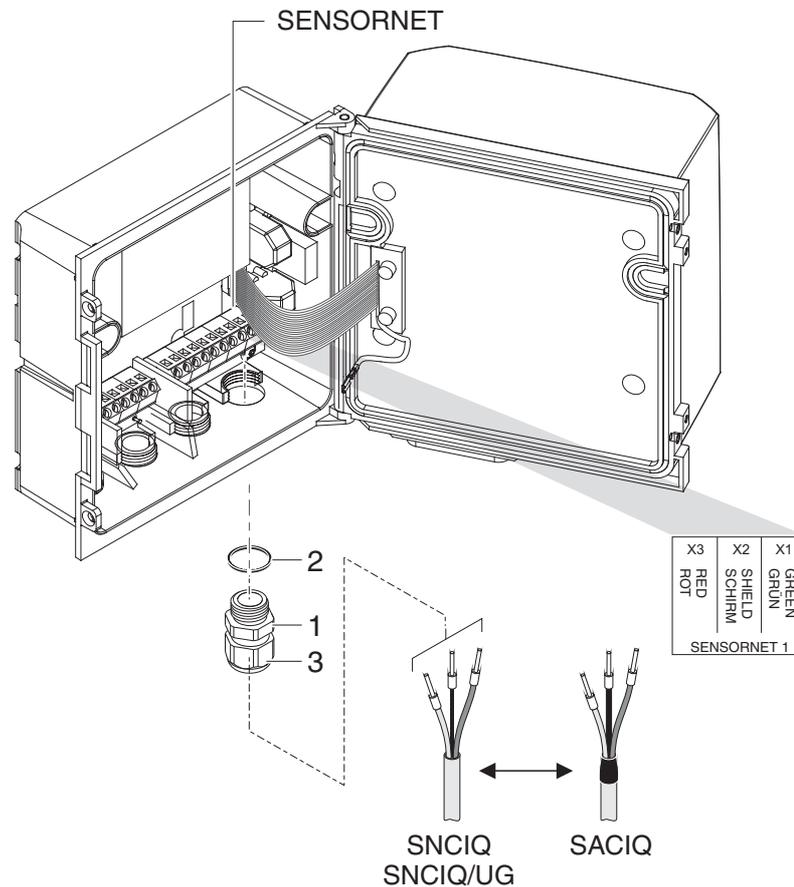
Kabel anschließen (Beispiel DIQ/S 28X-CR3)
